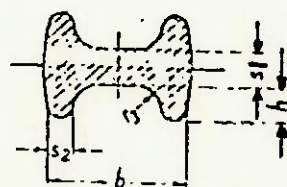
Esquema de peça indicando parâmetros de espessura, comprimento de parede e raio de curvatura.
